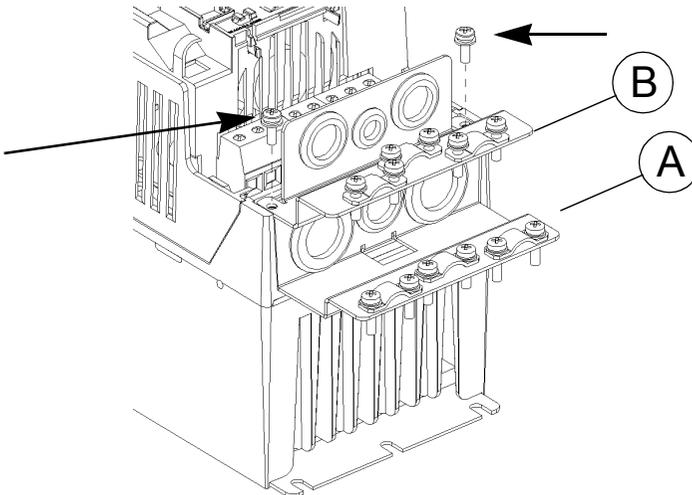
Durchführungsblech für Steuerkabel (B) montieren; Frequenzumrichter des Types IP 21 / NEMA1
